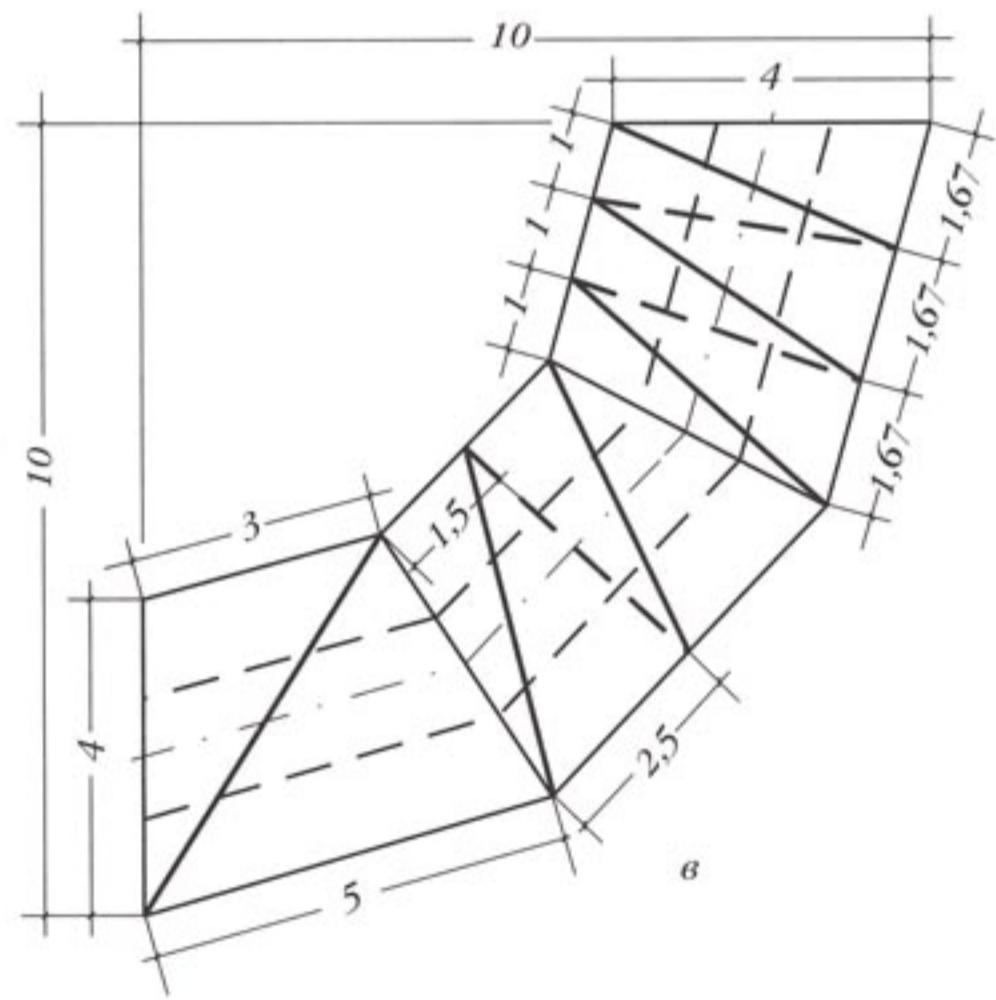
Чертеж и схема разметки основания двухсвечника к рис. 178
